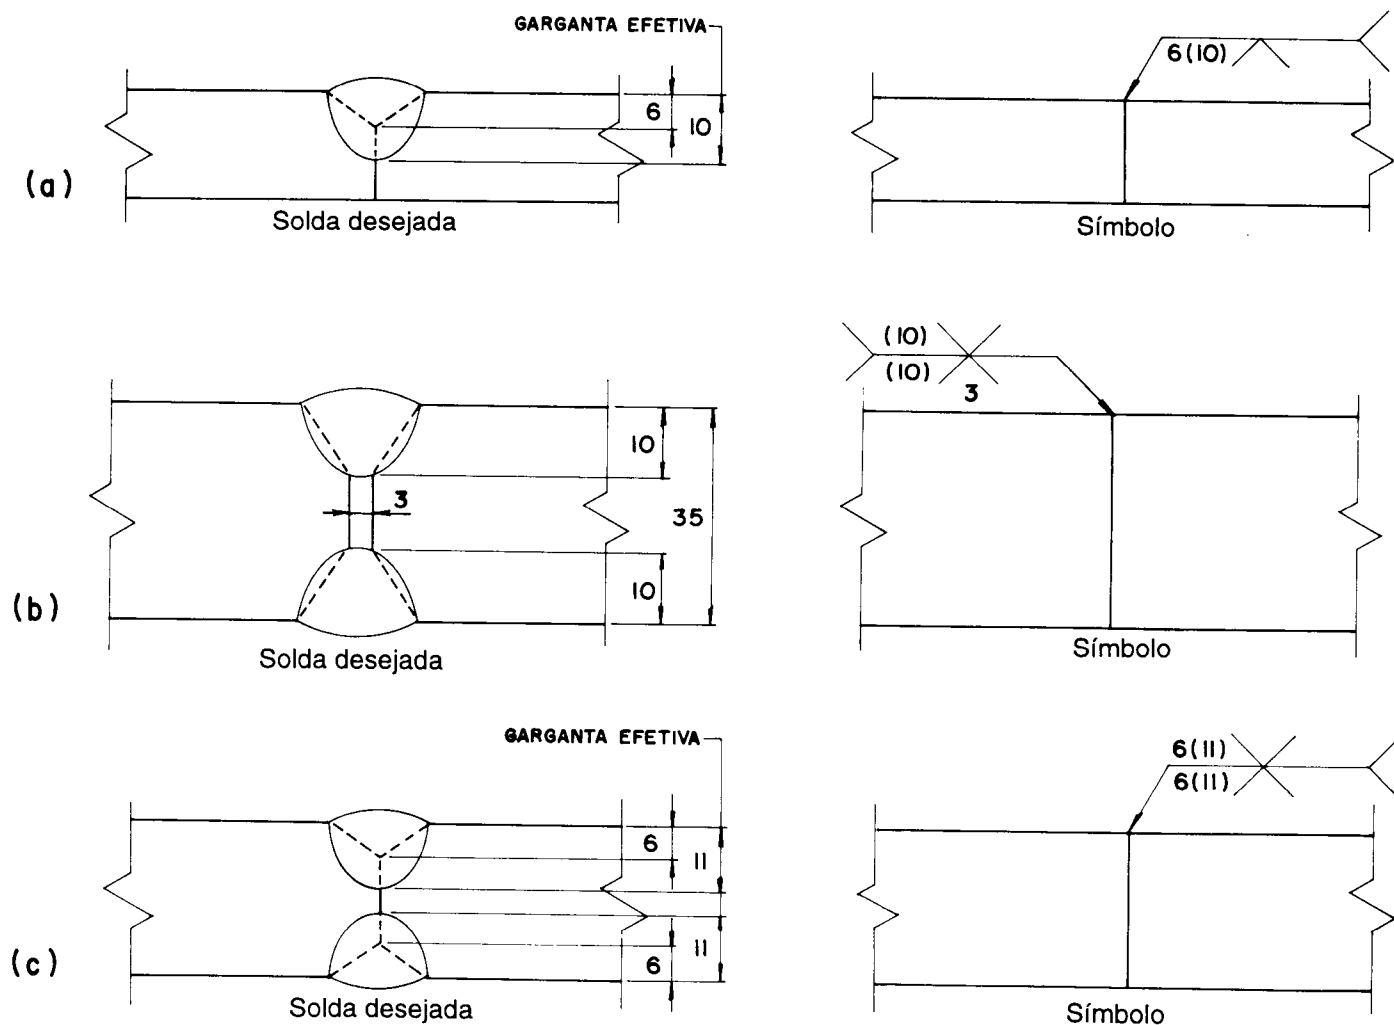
Exemplo de símbolos de soldagem de penetração parcial
